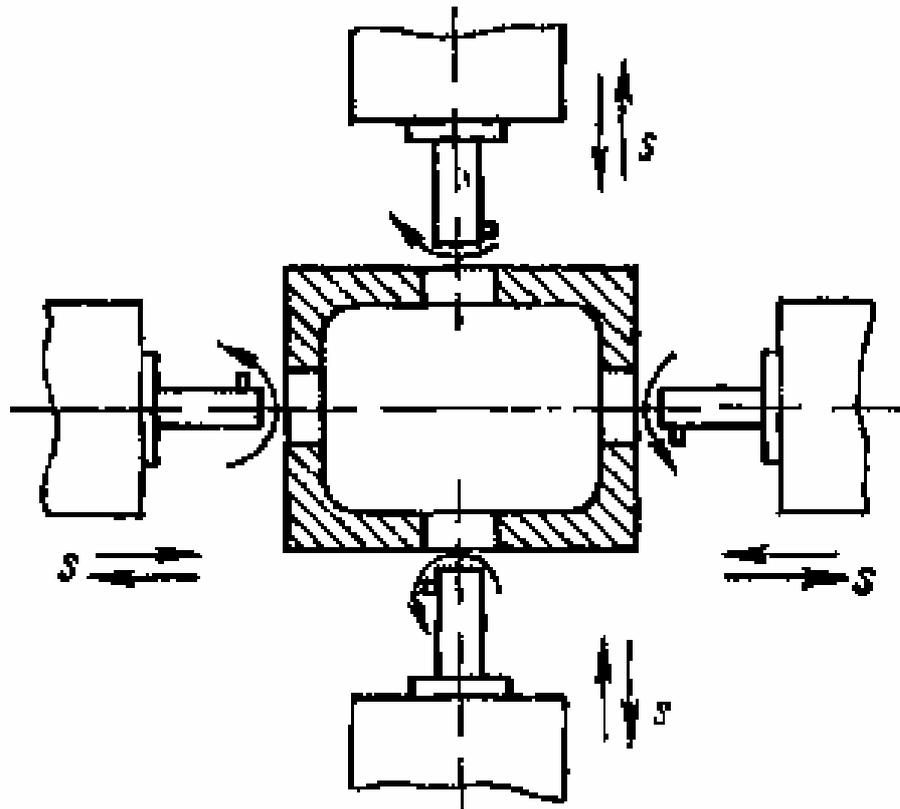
Схема обработки корпусной детали на агрегатном станке
